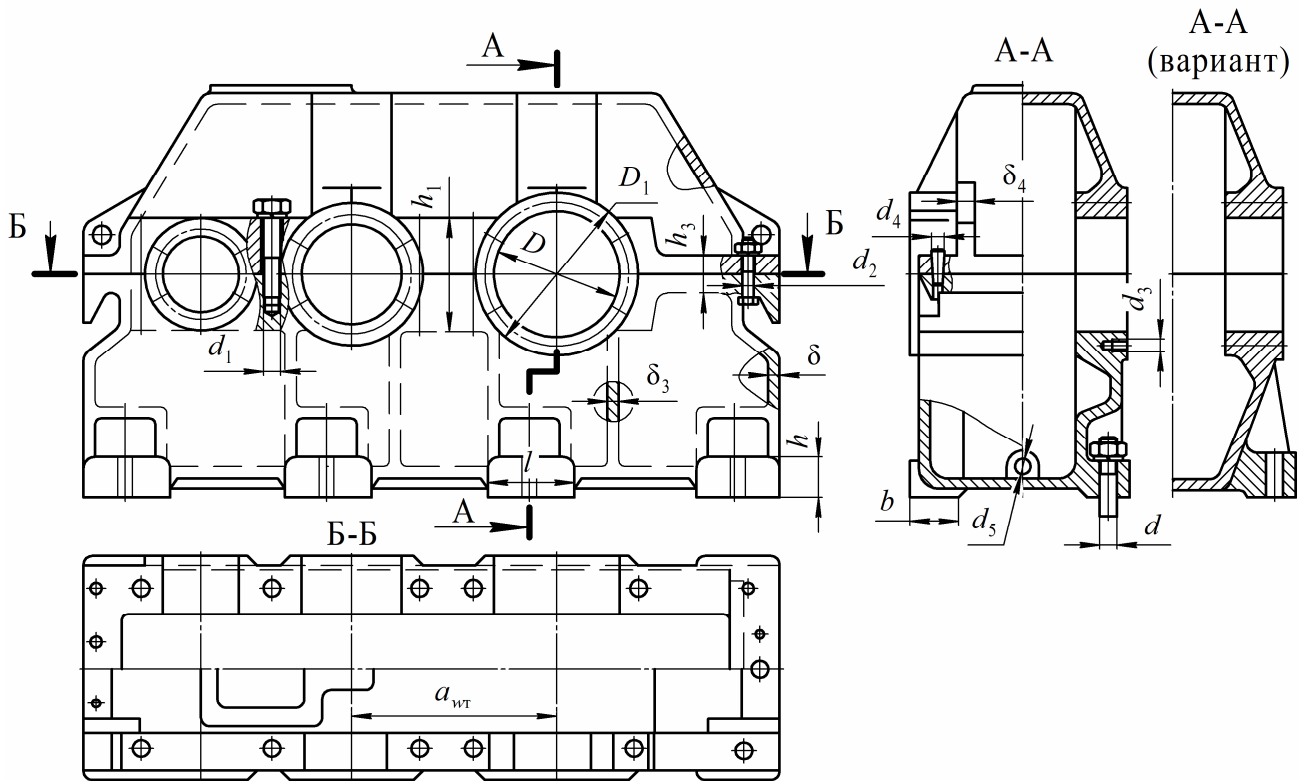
Конструкция корпуса двухступенчатого цилиндрического редуктора
